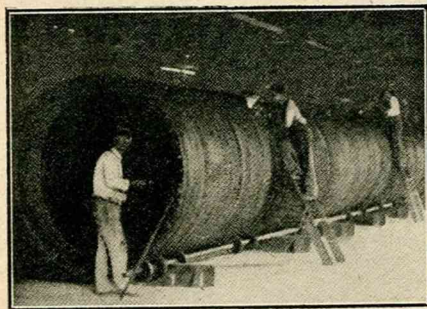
Soudure d'un élément du tube, long de 22 mètres. Une tige à galets guide le tube et le fait tourner.
